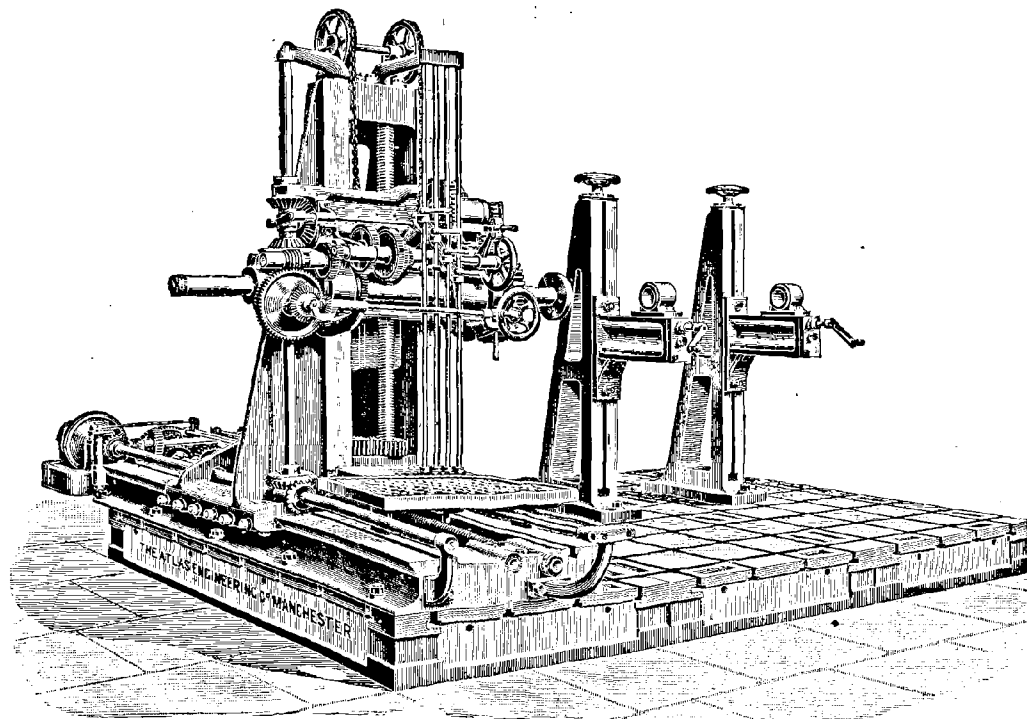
Machine universelle à aléser, percer et fraiser de M. Lucas.
